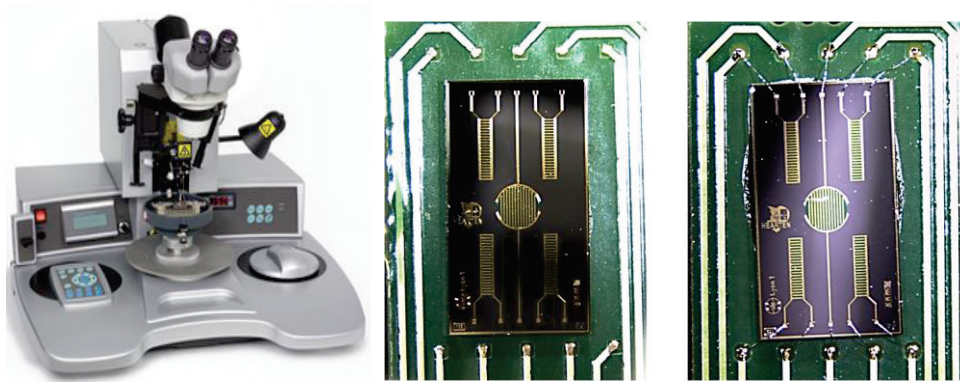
Appareil de soudure et vue des dispositifs avant et après soudure
